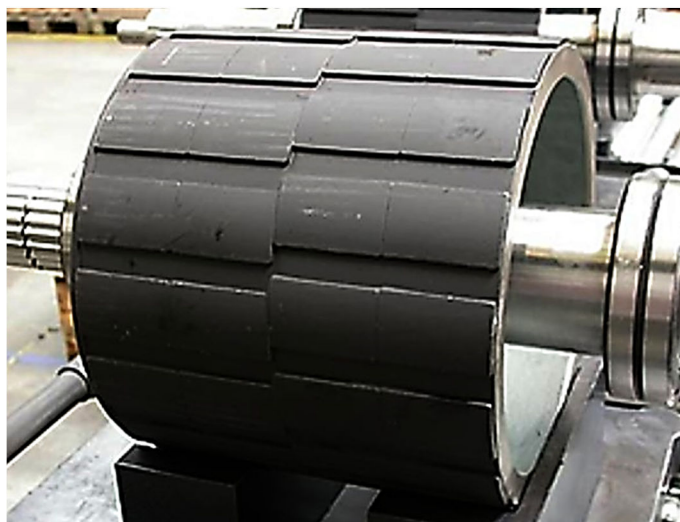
Внешний вид ротора вентильного электродвигателя лифтовой установки с постоянными магнитами
